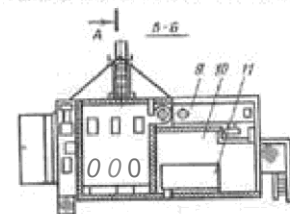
Шинносушилка передвижная ШП-0,06:
